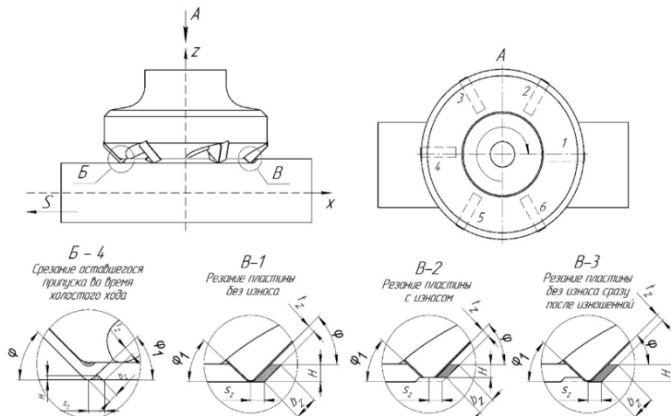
Схема процесса фрезерования чугунной поверхности при неравномерно износе режущих керамических пластин
